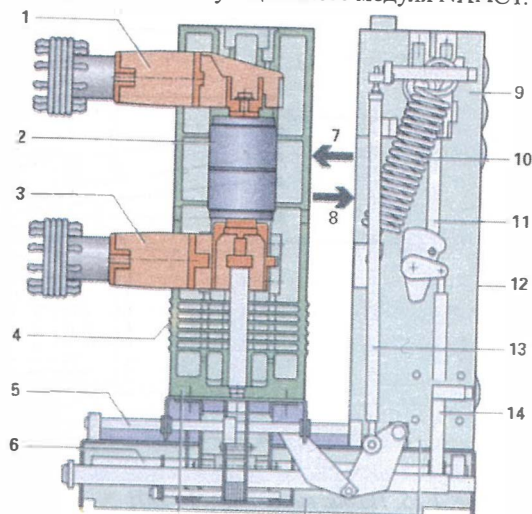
Кинематический чертеж вакуумного коммутационного модуля NXACT. 1 - верхний ввод, 2 - вакуумная камера, 3 - нижний ввод, 4 - корпус полюса, 5 - направляющая штанга для передвижения полюсов, 6 - полюсная кинематика, 7 - направление движения полюсов из положения разъединения в положение ввода в действие, 8 - направление движения полюсов из положения ввода в действие в положение разъединения, 9 - привод, 10 - включающая пружина, 11 - вал привода силового выключателя, 12 - панель управления, 13 - вал привода разъединения с механической блокировкой, 14 - вал привода заземлителя с механической блокировкой.
